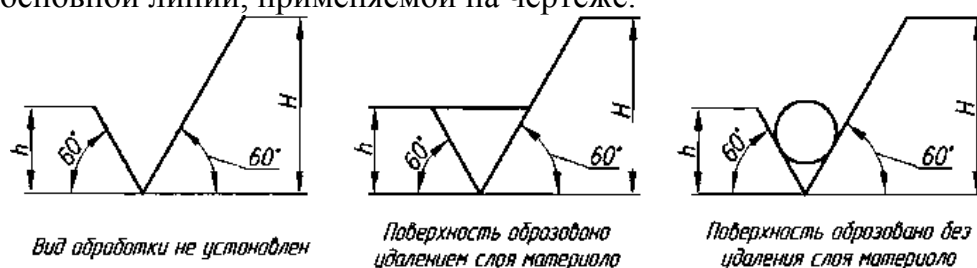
Знаки для обозначения шероховатости поверхности
